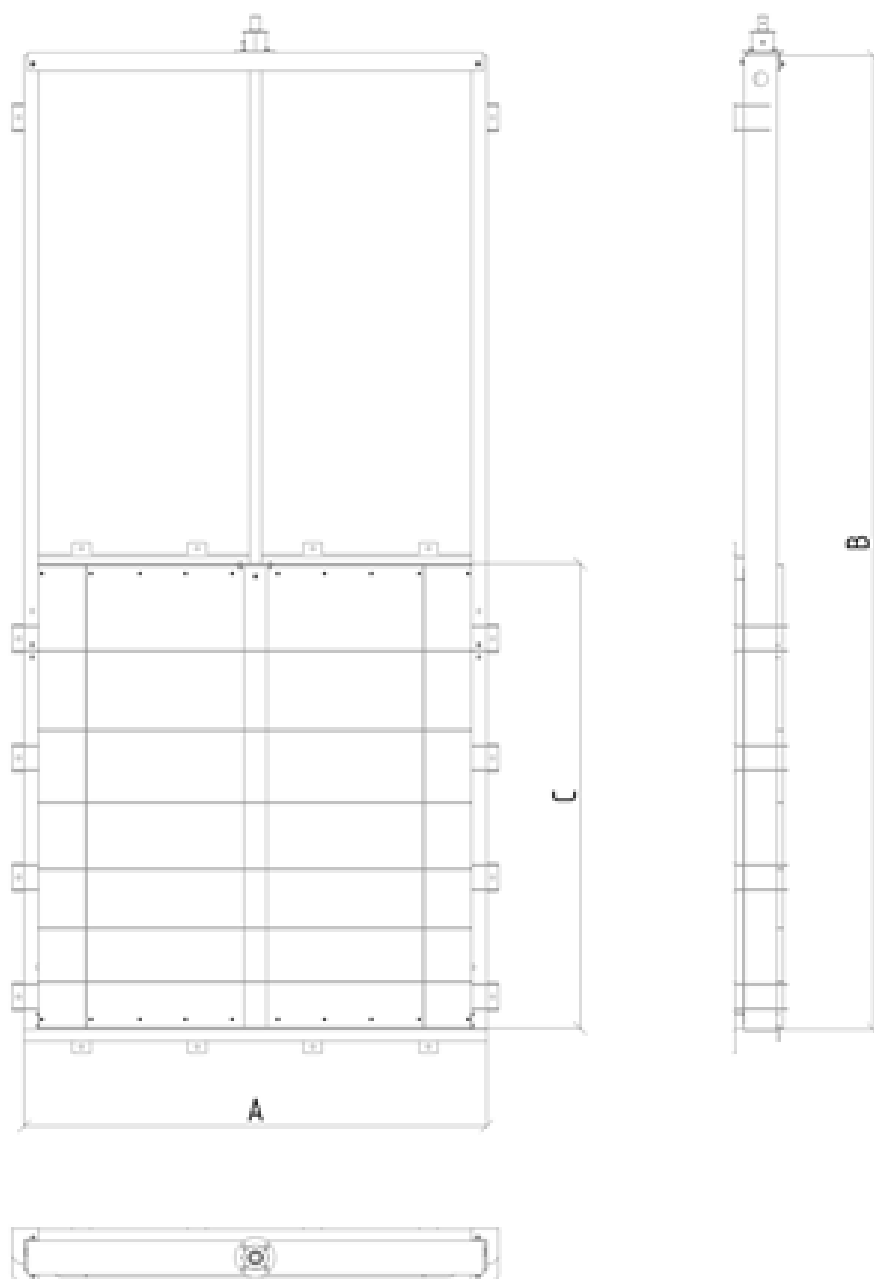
Габаритные размеры затвора щитового глубинного
